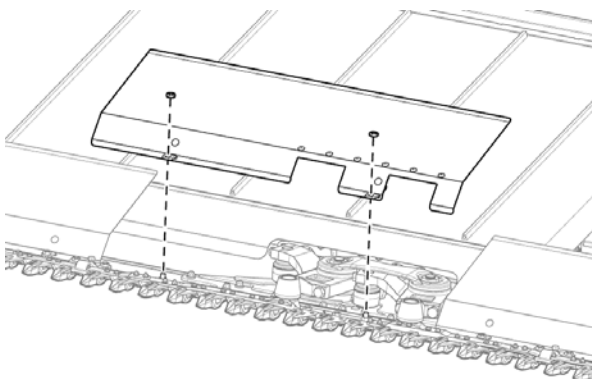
Снятие перьевой пластины, расположенной над подшипниками ножей.
